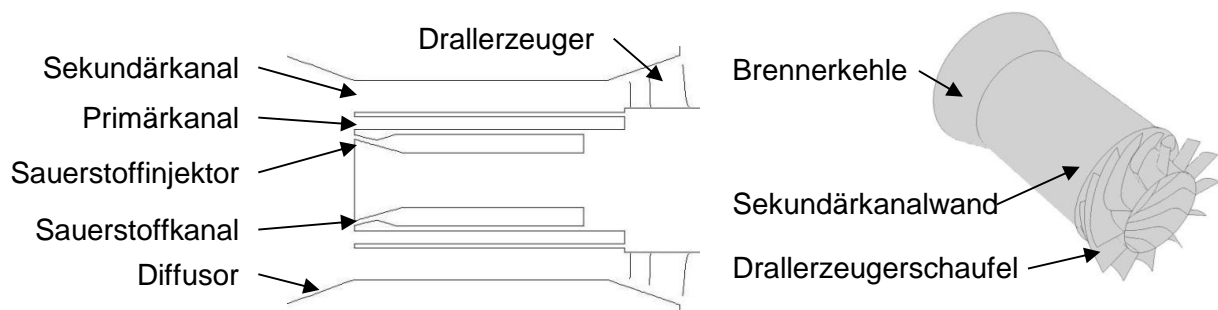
Schnitt durch den Brenner mit den zugehörigen Zuströmkanälen (links) und Detaildarstellung des Drallerzeugerschaukelgitters (rechts)
